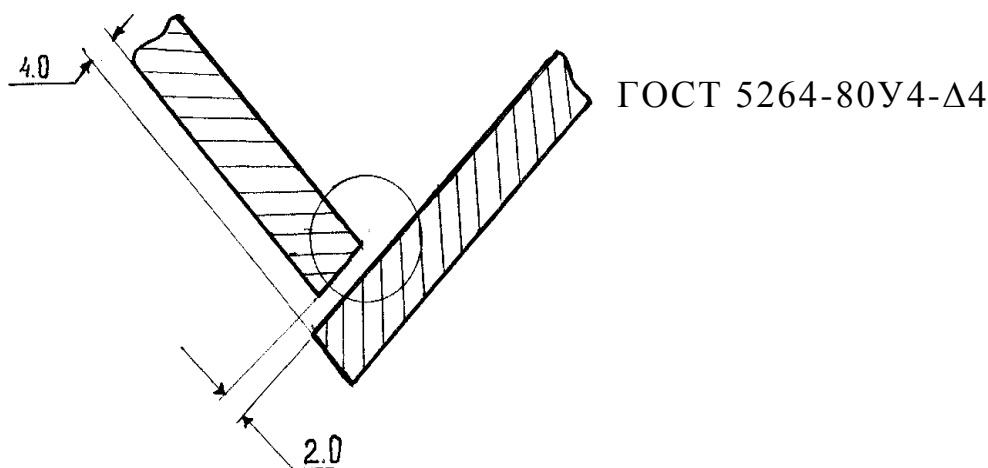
Эскиз сварного соединения пластин под углом 45°
